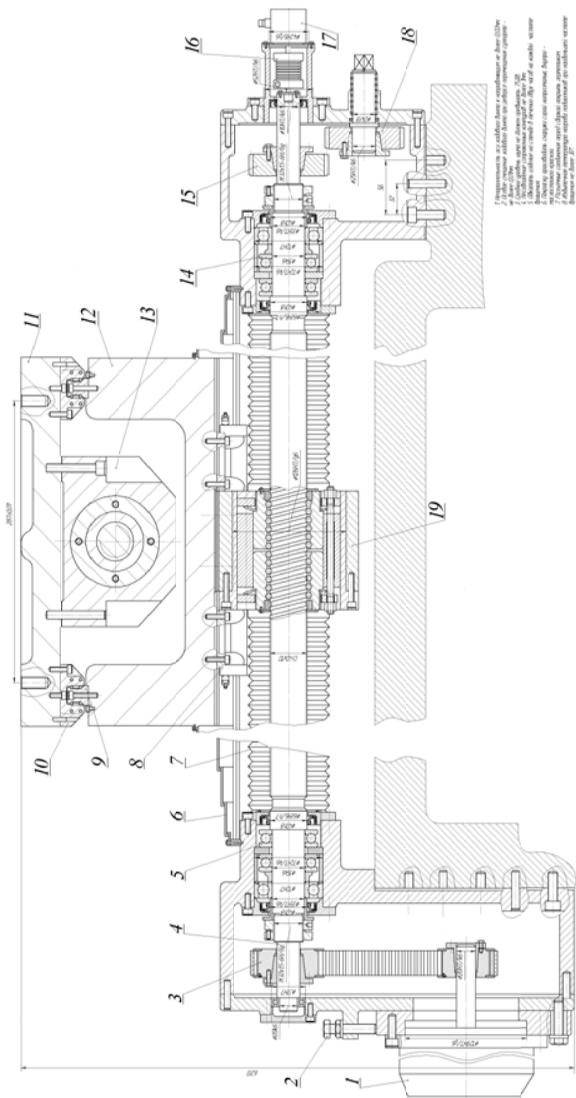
Крестовый суппорт 11 с горизонтальным приводом продольной подачи салазок 12 токарного станка с ЧПУ: с механическим редуктором с электродвигателем 1, ременной зубчатой передачей 3 и регулировочным винтом 2 натяжения ремня; обемными фиксирующими опорами ходового винта 4 с комплектом из двух упорных и радиального шариковых подшипников 5 и 14; телескопической защитой направляющих 6 и гармоникообразной – ходового винта 7; рельсовыми шариковыми направляющими с циркуляцией тел качения с каретками 8 и 9 и шинами 10; тяговым механизмом привода поперечной подачи 13 суппорта; цилиндрическим зубчатым редуктором ручных перемещений с колесами 15 и 18 и муфтой 16 датчика обратной связи 17; передачей винт-гайка качения с двумя гайками со специальным механизмом создания предварительного натяга 19
